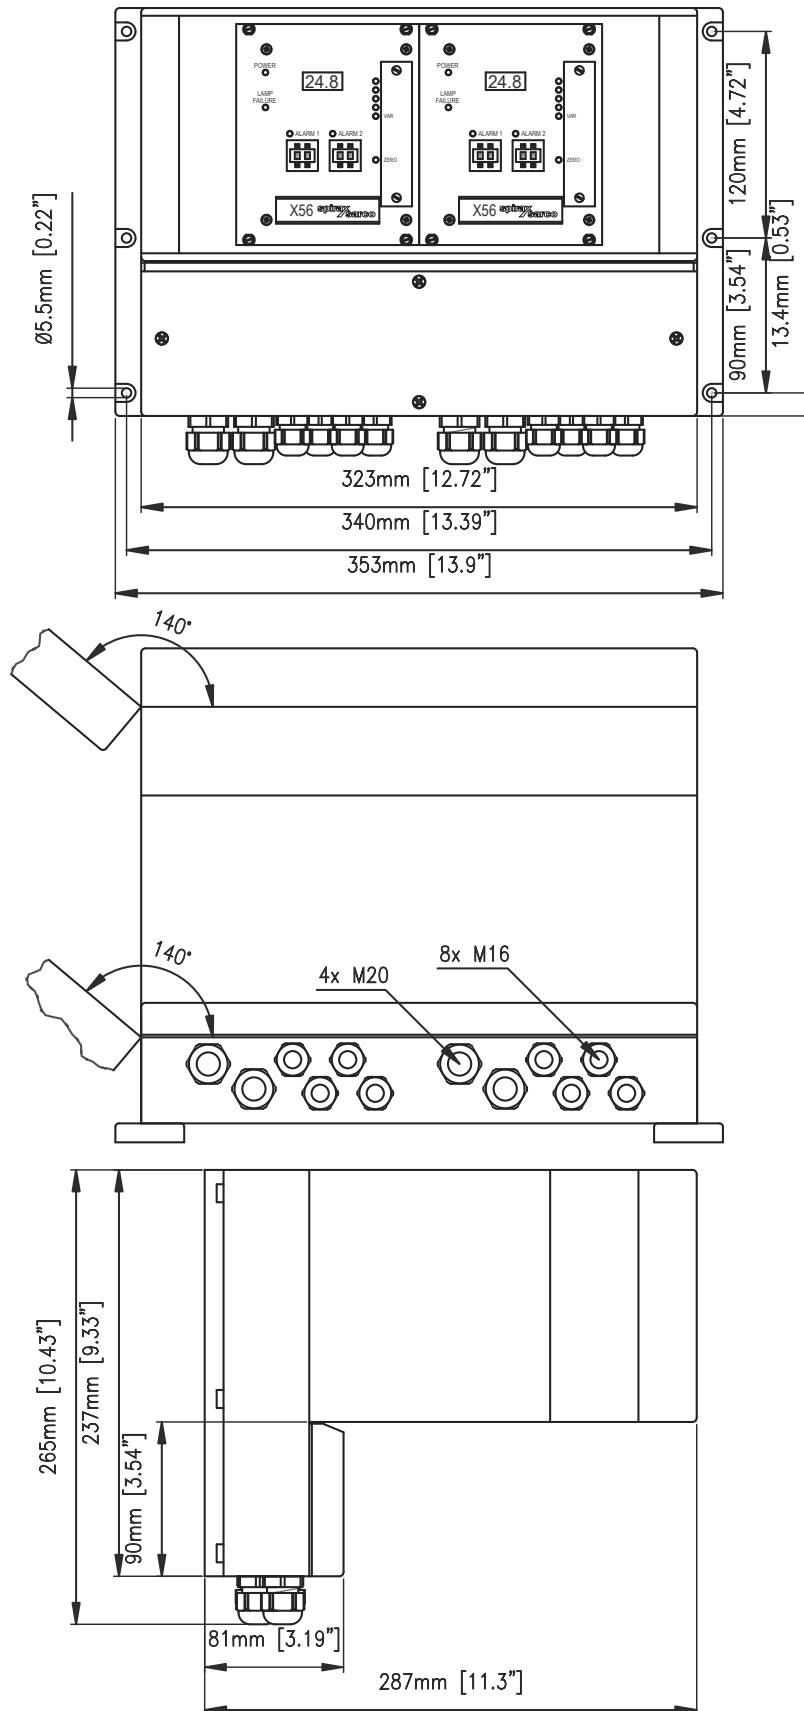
Dimensions avec boîtier B19-42 pour montage mural
